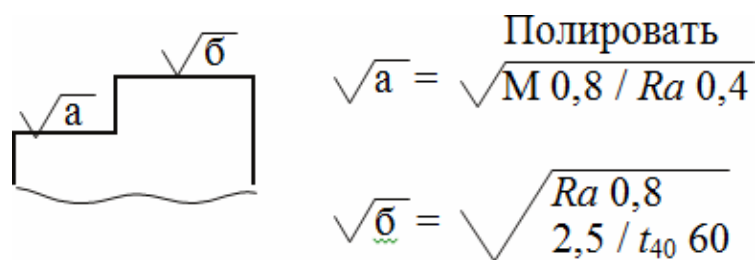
Пример упрощённого обозначения шероховатости поверхности
